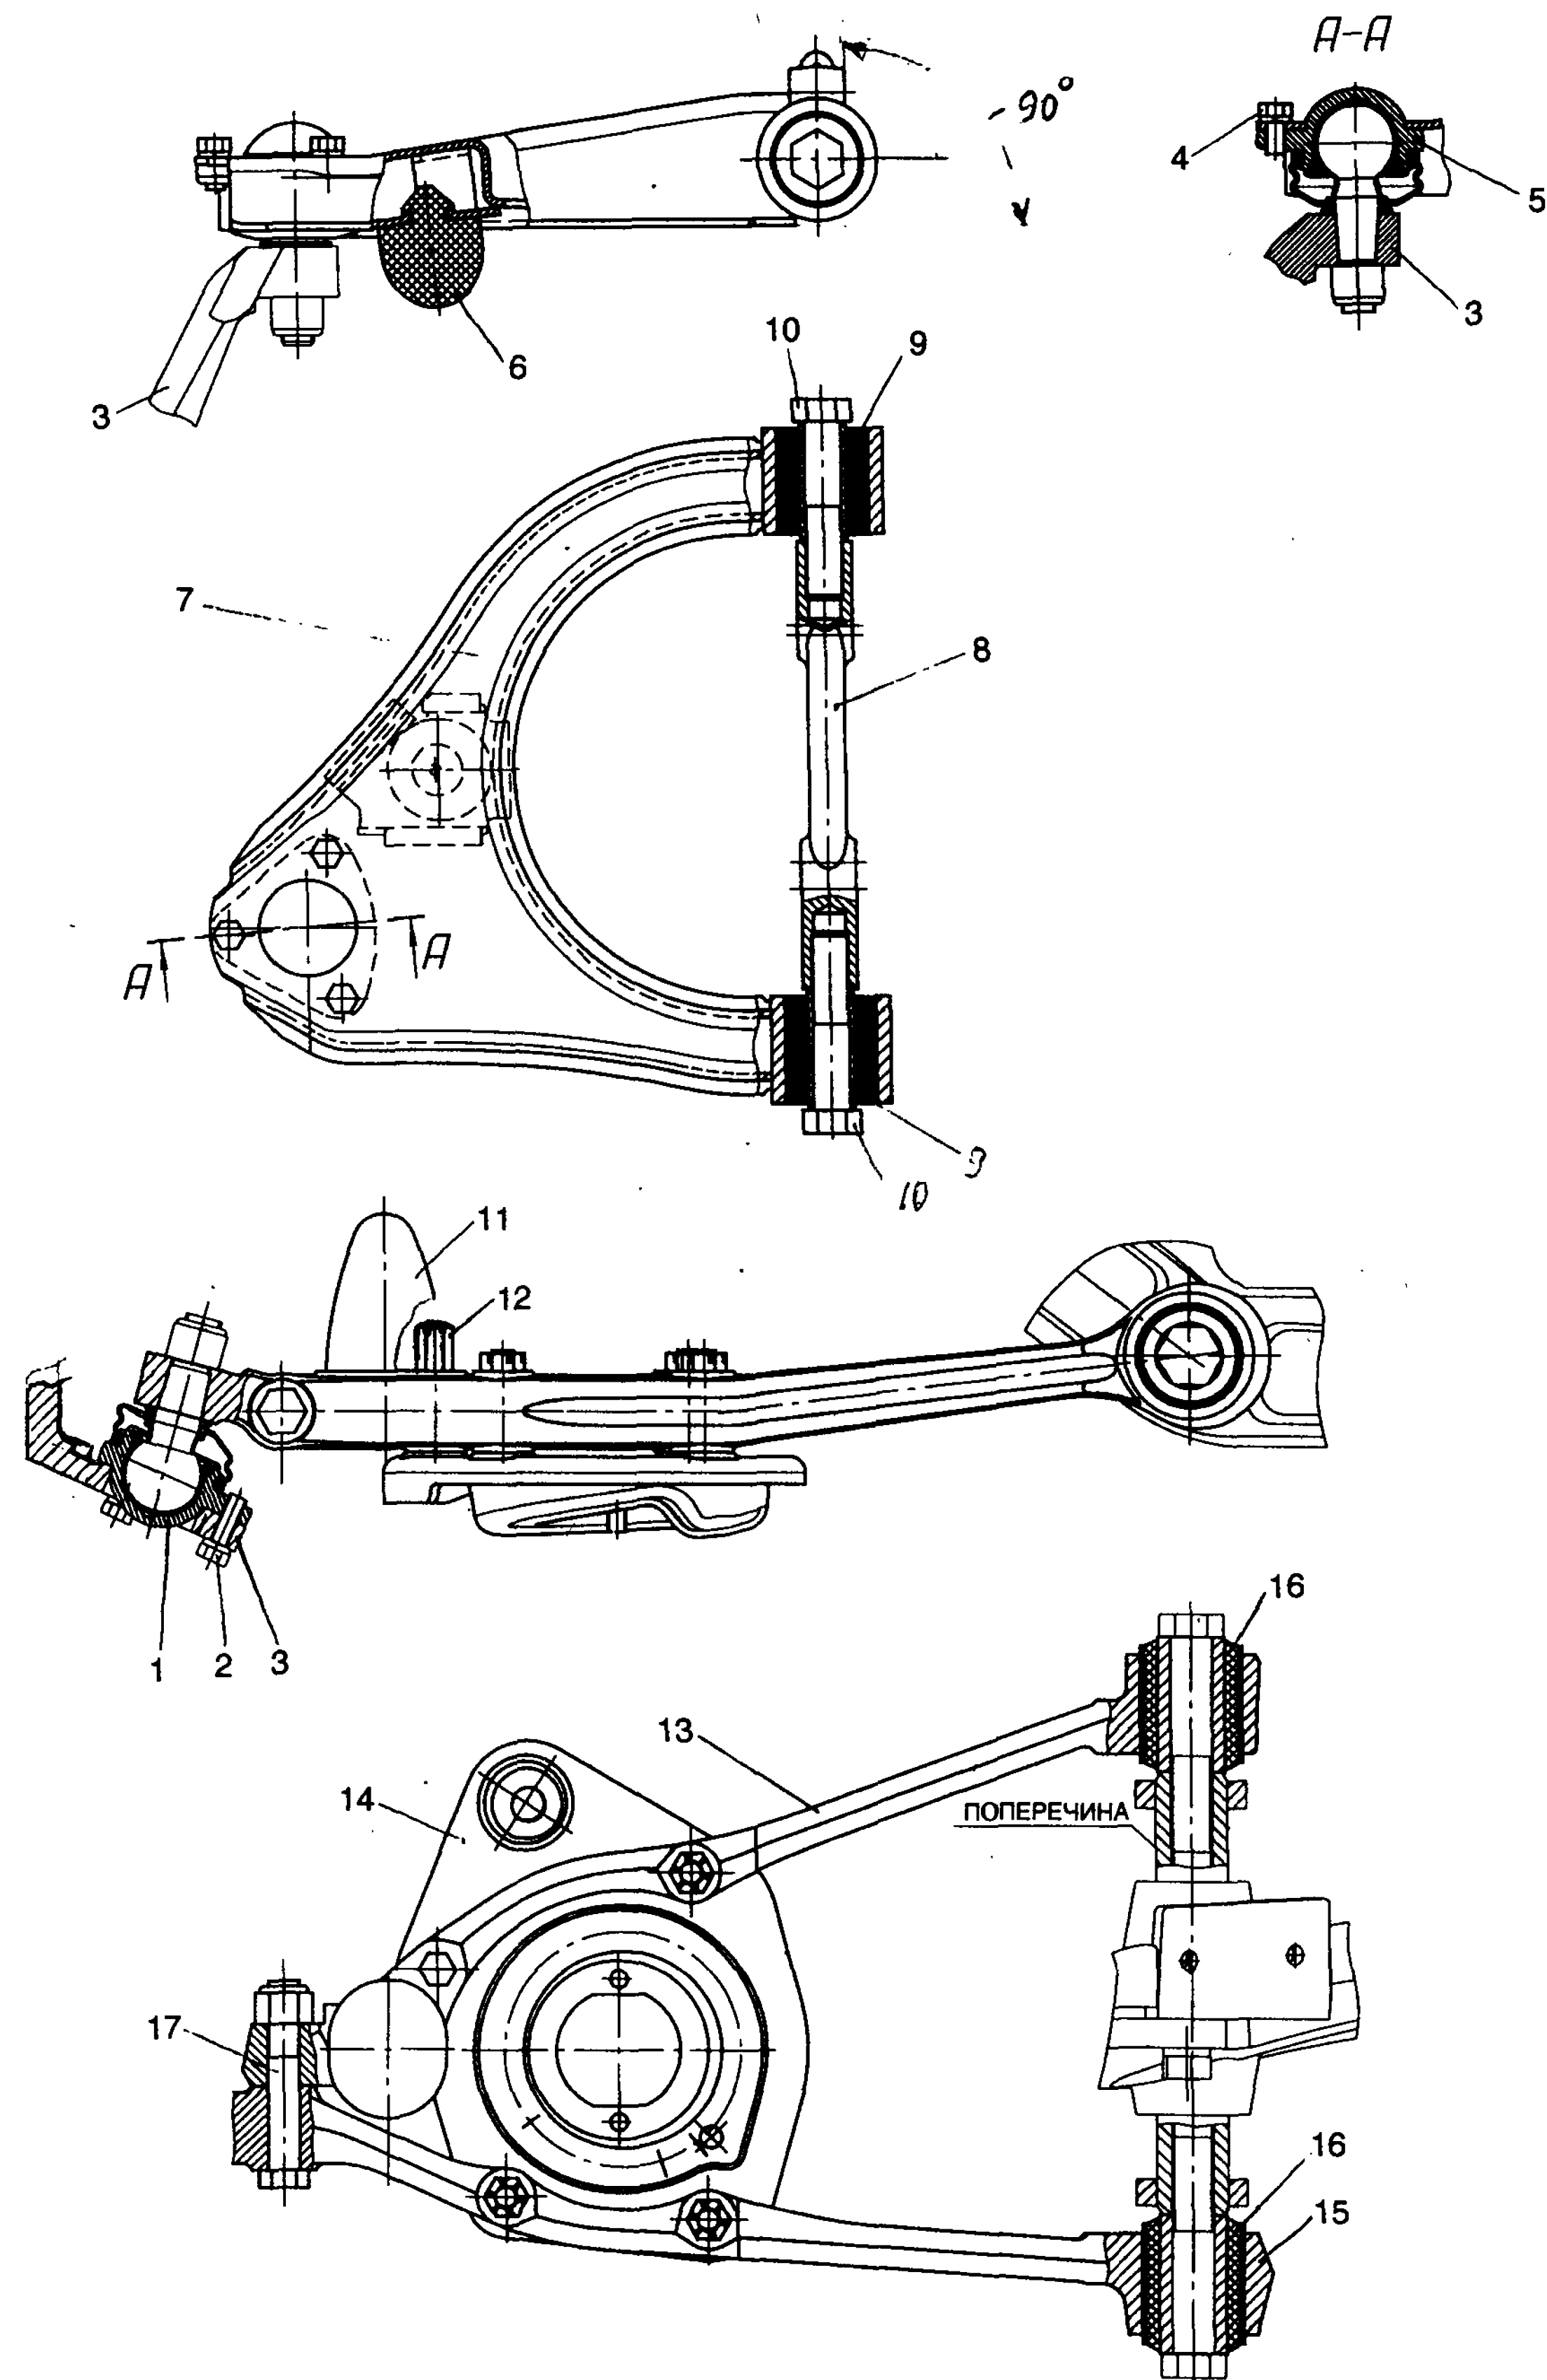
Верхний и нижний рычаги передней подвески и их крепление: 1 – шарнир шаровой нижней; 2 – болт крепления шарнира нижнего; 3 – стойка поворотная; 4 – болт крепления шарнира верхнего; 5 – шарнир шаровой верхней; 6 – буфер хода отдачи; 7 – рычаг верхний; 8 – ось верхних рычагов; 9 – сайлентблок верхнего рычага; 10 – болт крепления сайлентблока верхнего рычага; 11 – буфер хода сжатия; 12 – болт ограничительный; 13 – рычаг нижний передний; 14 – чашка пружины; 15 – рычаг нижний задний; 16 – сайлентблок нижнего рычага; 17 – болт стяжной нижних рычагов
